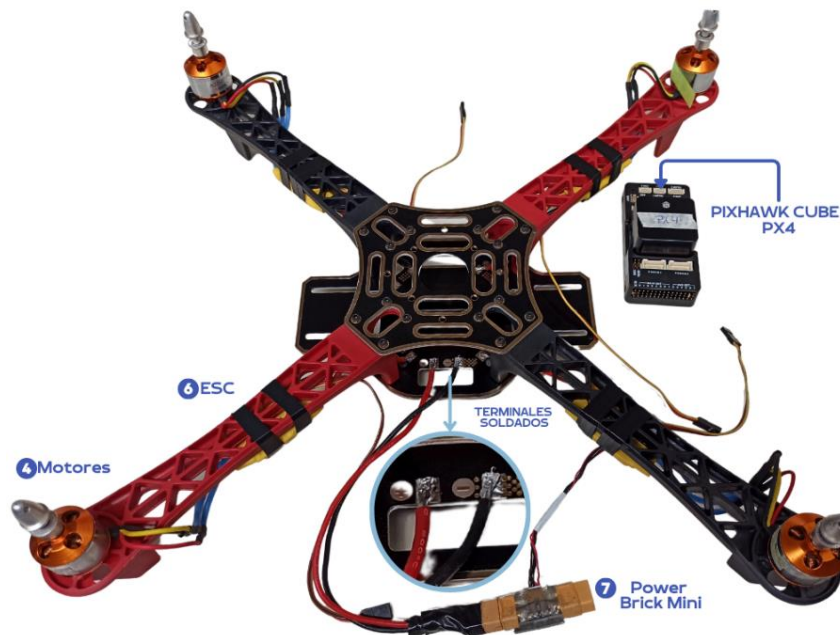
Ubicación de ESCs y soldadura de Power Brick Mini [Fuente propia]
